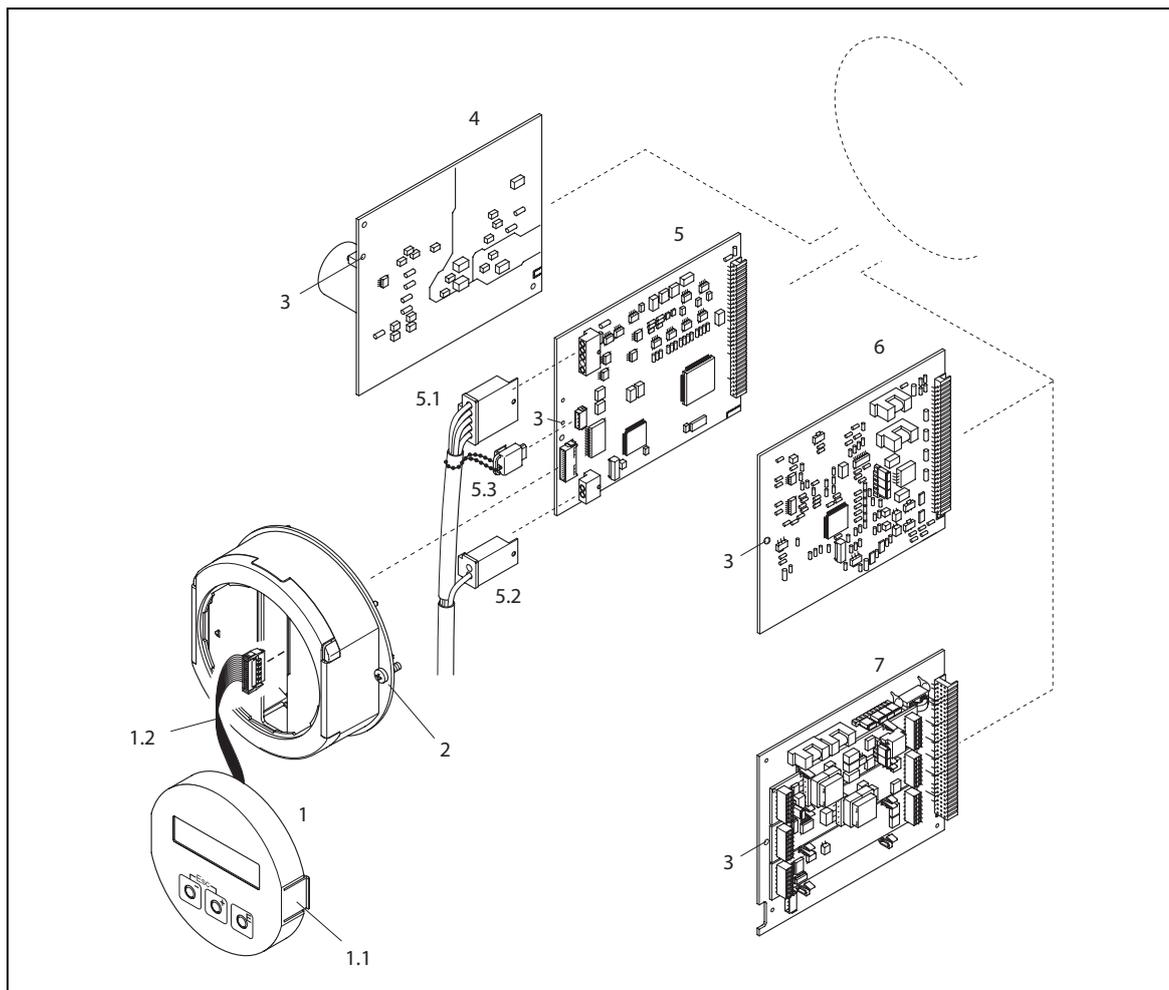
Корпус полевого блока: снятие и установка печатных плат
